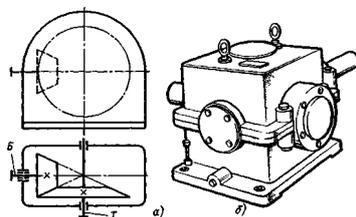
Редуктор конический: а) схема кинематическая, б) общий вид
